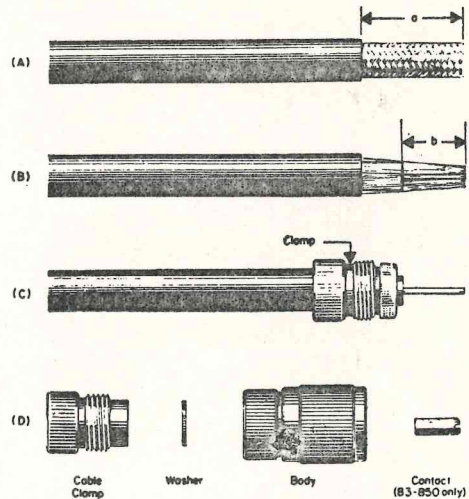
Instrucciones para acoplar adecuadamente conectores sin soldar y semisoldados Amphenol 83-850 y 83-851. Recortar la cubierta de vinilo del cable como se ve en (A). Para el 83-850, la dimensión a es de 15/16 de pulgada y para el 83-851 de 31/32 de pulgada. Peinar el trenzado como se ve en (B) y cortar el dieléctrico de forma que la dimensión b sea de 35/64 de pulgada para el tipo 83-850 y de 5/8 de pulgada para el 83-851. (Estar, solo en el 83-851, previamente el conductor central.) Poner el trenzado en forma de punta, como se ve. Atornillar la abrazadera a la cubierta del cable hasta que sus salientes interiores topen contra el extremo de la cubierta. Plegar el trenzado hacia la abrazadera, amoldándolo a ésta y alisándolo hasta que quede como se ve en (C). Colocar una arandela dentro de la cavidad del cuerpo y atornillar éste fuertemente en la abrazadera. Para el 83-850 solo atornillar la patilla de contacto de forma que encaje en su interior al conductor central. Para el 83-851 soldar suavemente el conductor central a la patilla de contacto con rapidez y cuidado para no destruir el aislante.
